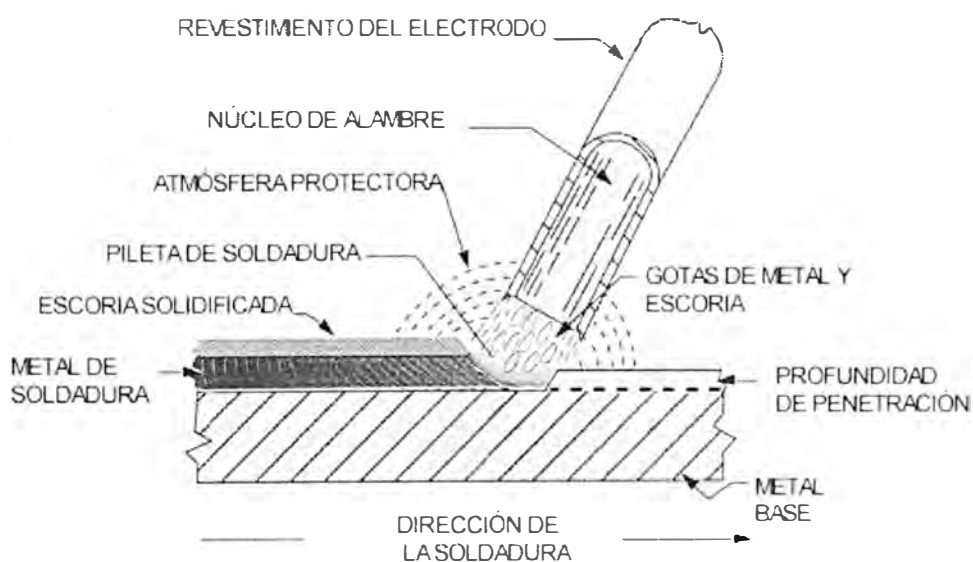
Soldadura por Arco con Electrodo Revestido
